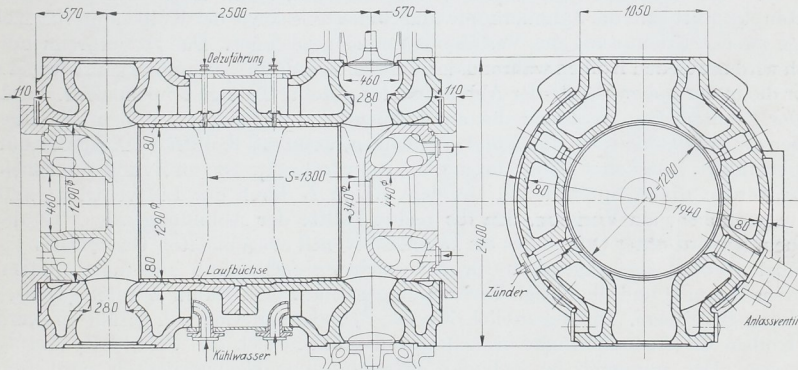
Großgasmaschinenzylinder von Ehrhardt und Sehmer. M. 1:50.
